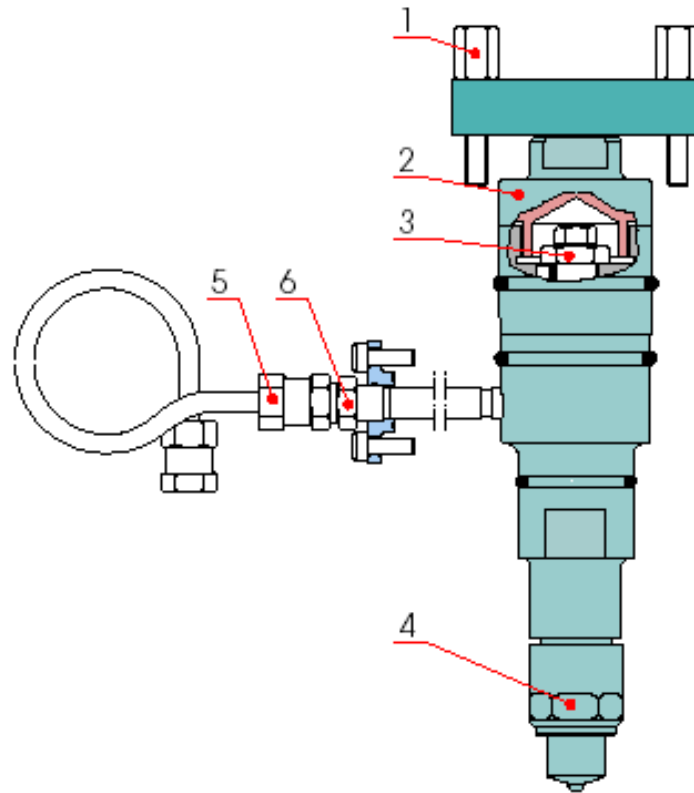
Cuerpo del inyector de combustible y sus partes
